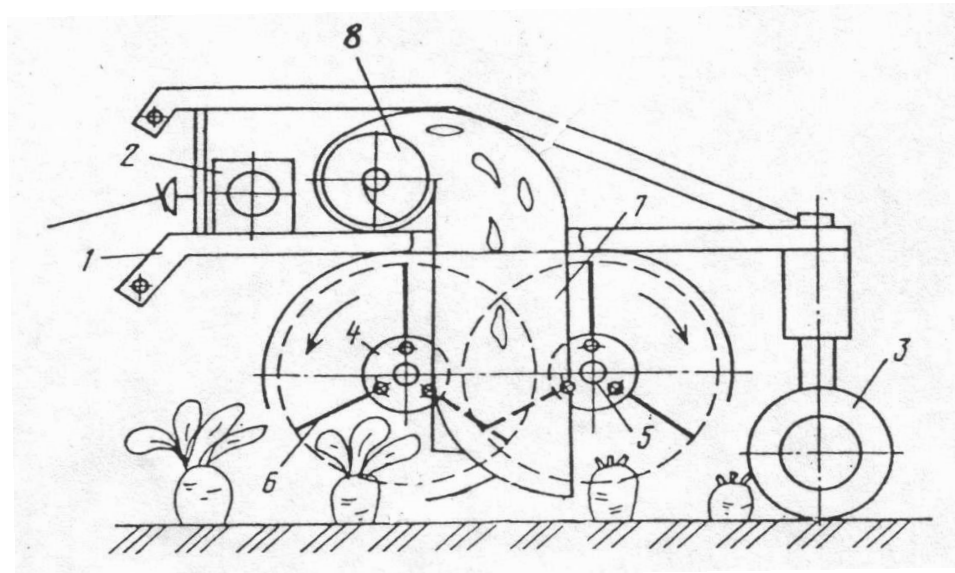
Схема очисника згідно а.с. № 1568927: 1-рама; 2- механізм приводу; 3- опорні колеса; 4,5- передній і задній вали; 6 – еластичні робочі органи; 7- кожух; 8- шнек
